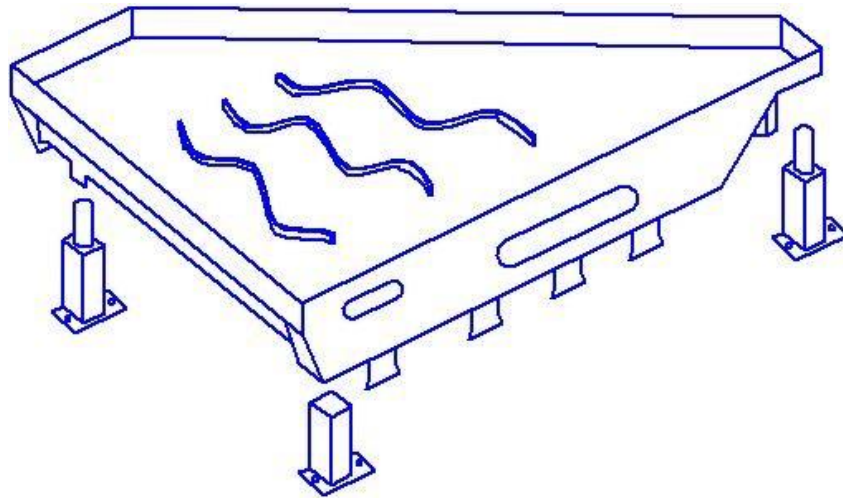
Конструктивна схема ПСС з розташованими на робочій поверхні інтенсифікаторами хвилеподібного типу
